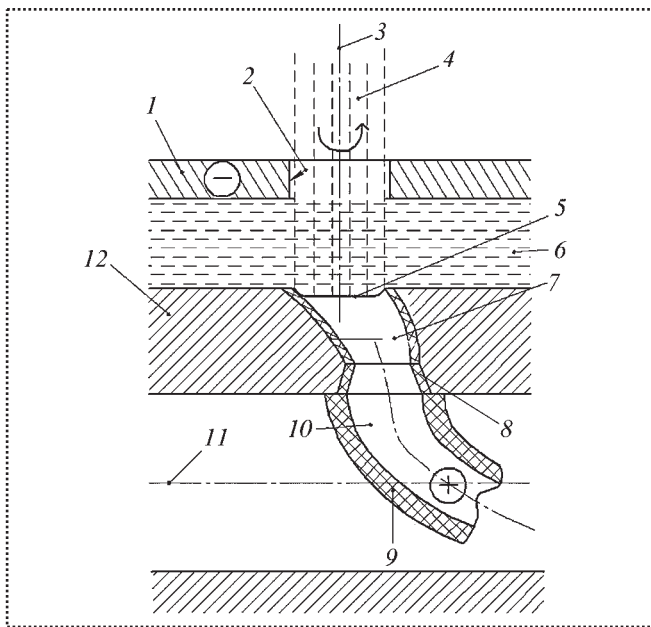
Схема комбинированного удаления вставки из керамической форсунки:
